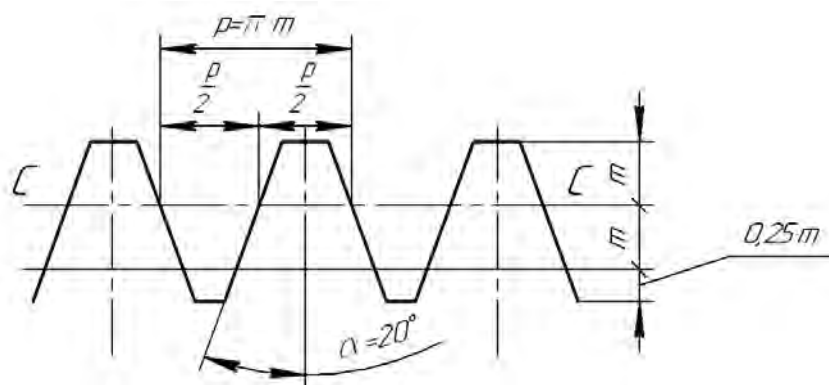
Основные параметры профиля зуба зубчатой рейки
